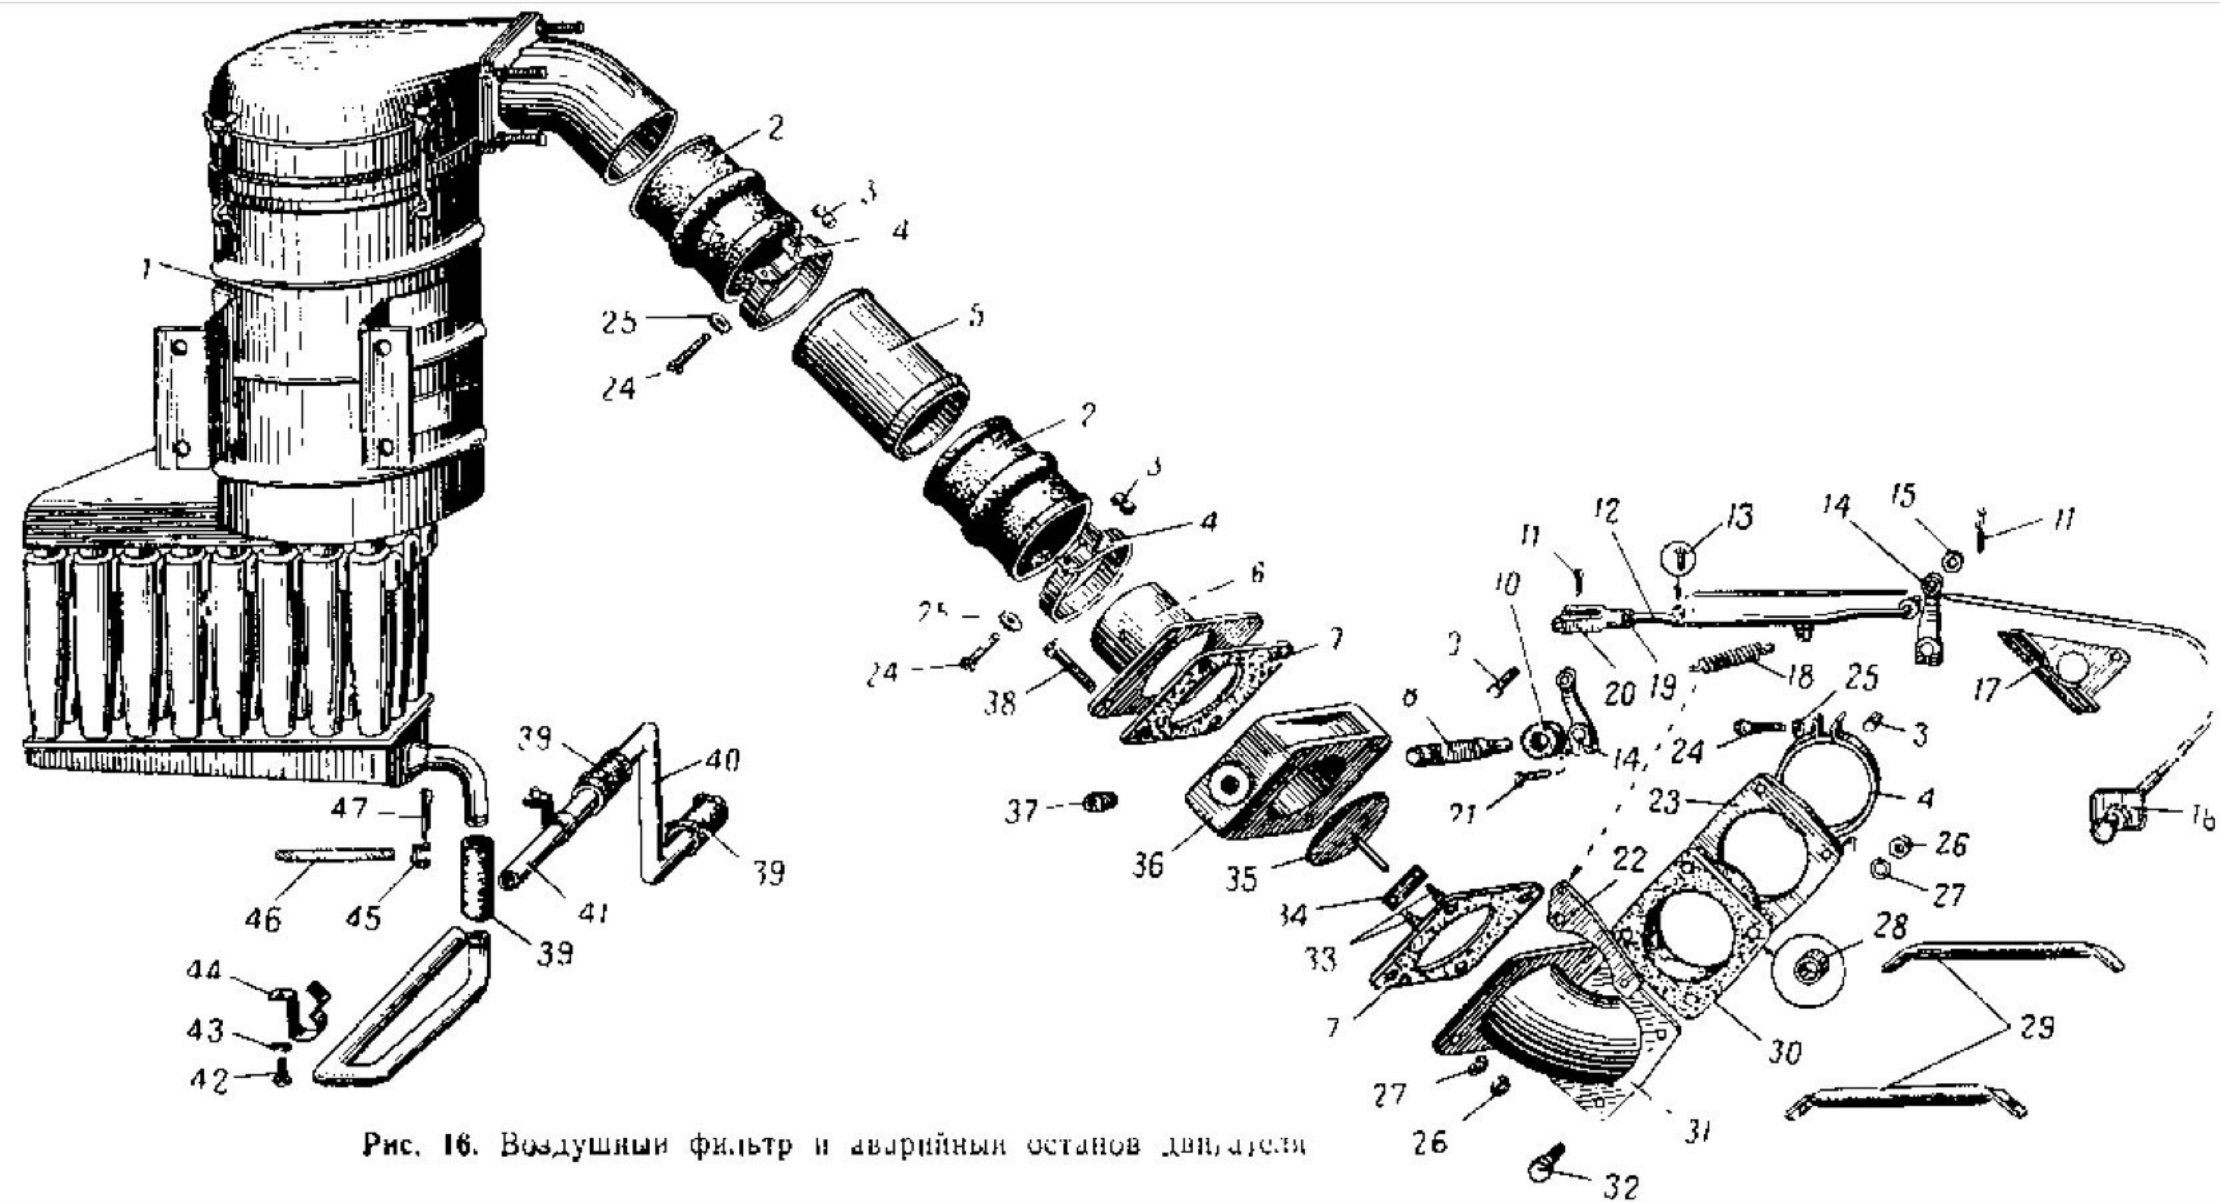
Воздушный фильтр и аварийный останов двигателя
